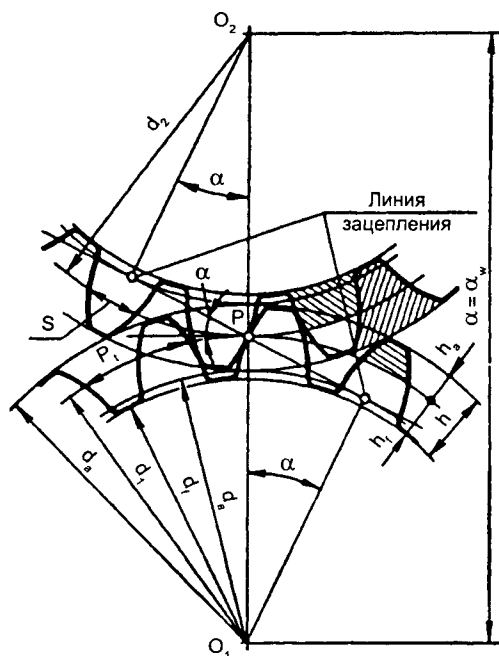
Принципиальная схема зубчатой передачи и геометрии зубчатого зацепления прямозубых цилиндрических колес
